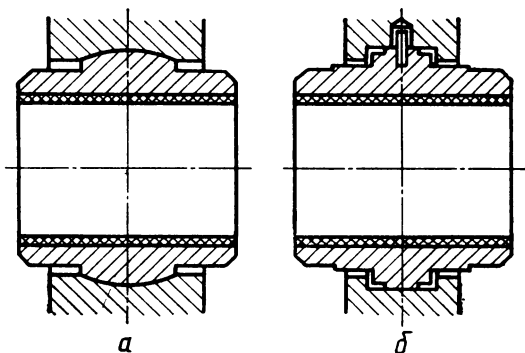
Схемы самоустанавливающихся подшипников скольжения
